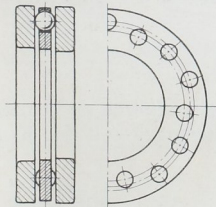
Längslager mit ebenen Laufflächen. Kugelfabrik Fischer.
